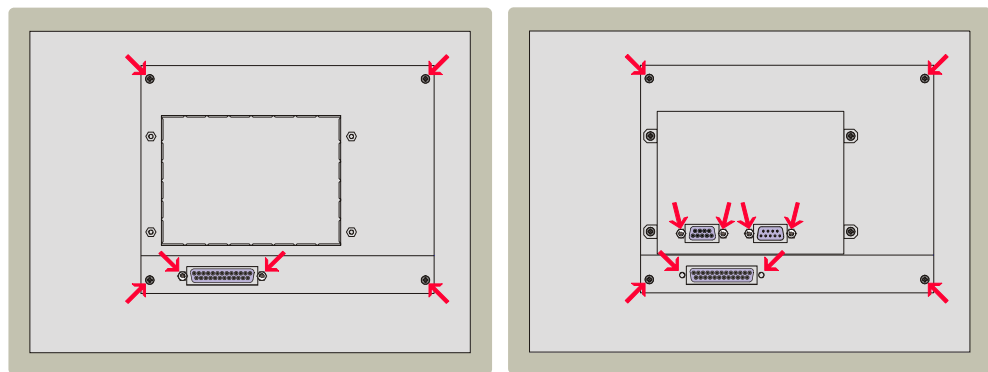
Schrauben am Standardgerät (links) / Feldbusgerät (rechts)
